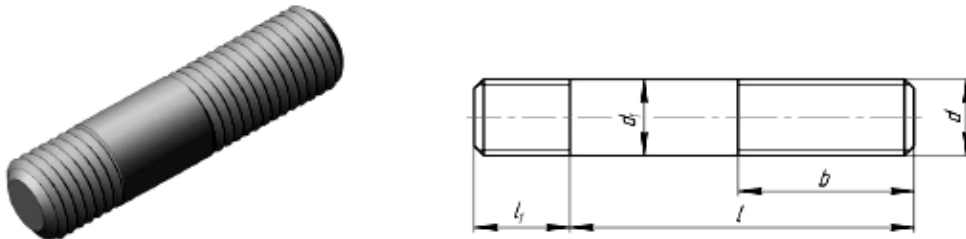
Шпилька общего назначения исполнения 1
